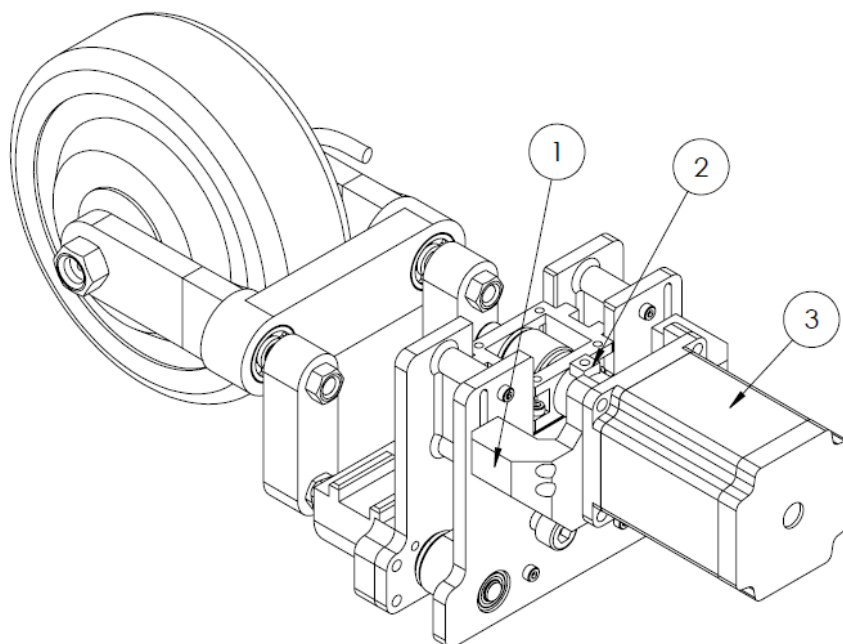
Механізм балансування пристрою: 1) кріплення крокового двигуна; 2) муфта жорстка; 3) кроковий двигун
